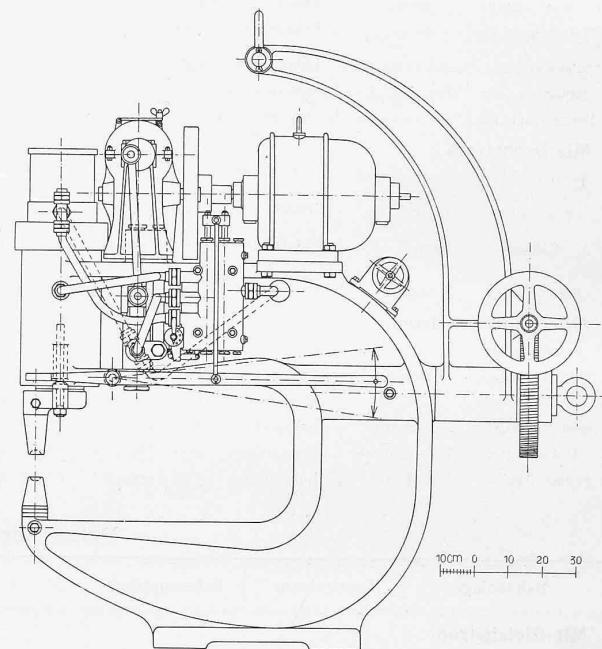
Geometrische Ansicht der Nietmaschine. — 1 : 20.
